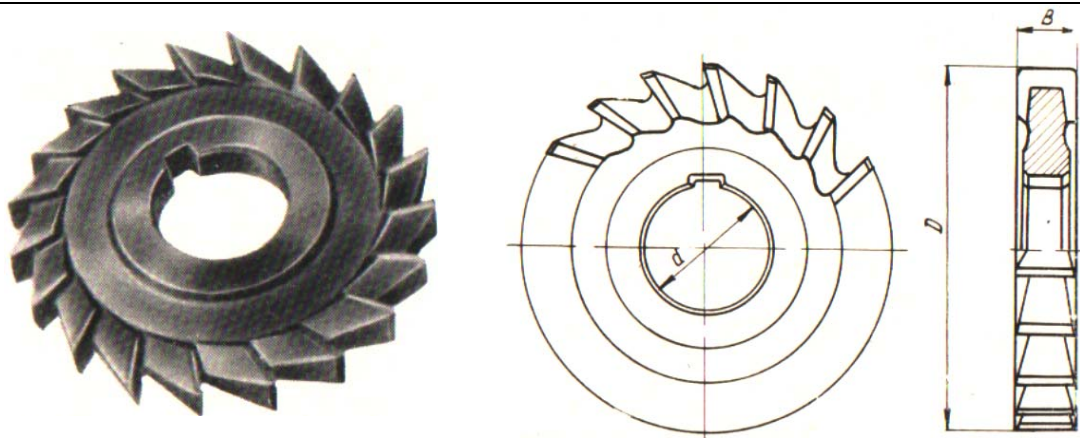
Современная конструкция цельной дисковой фрезы с торцовыми зубьями прямобочного профиля
